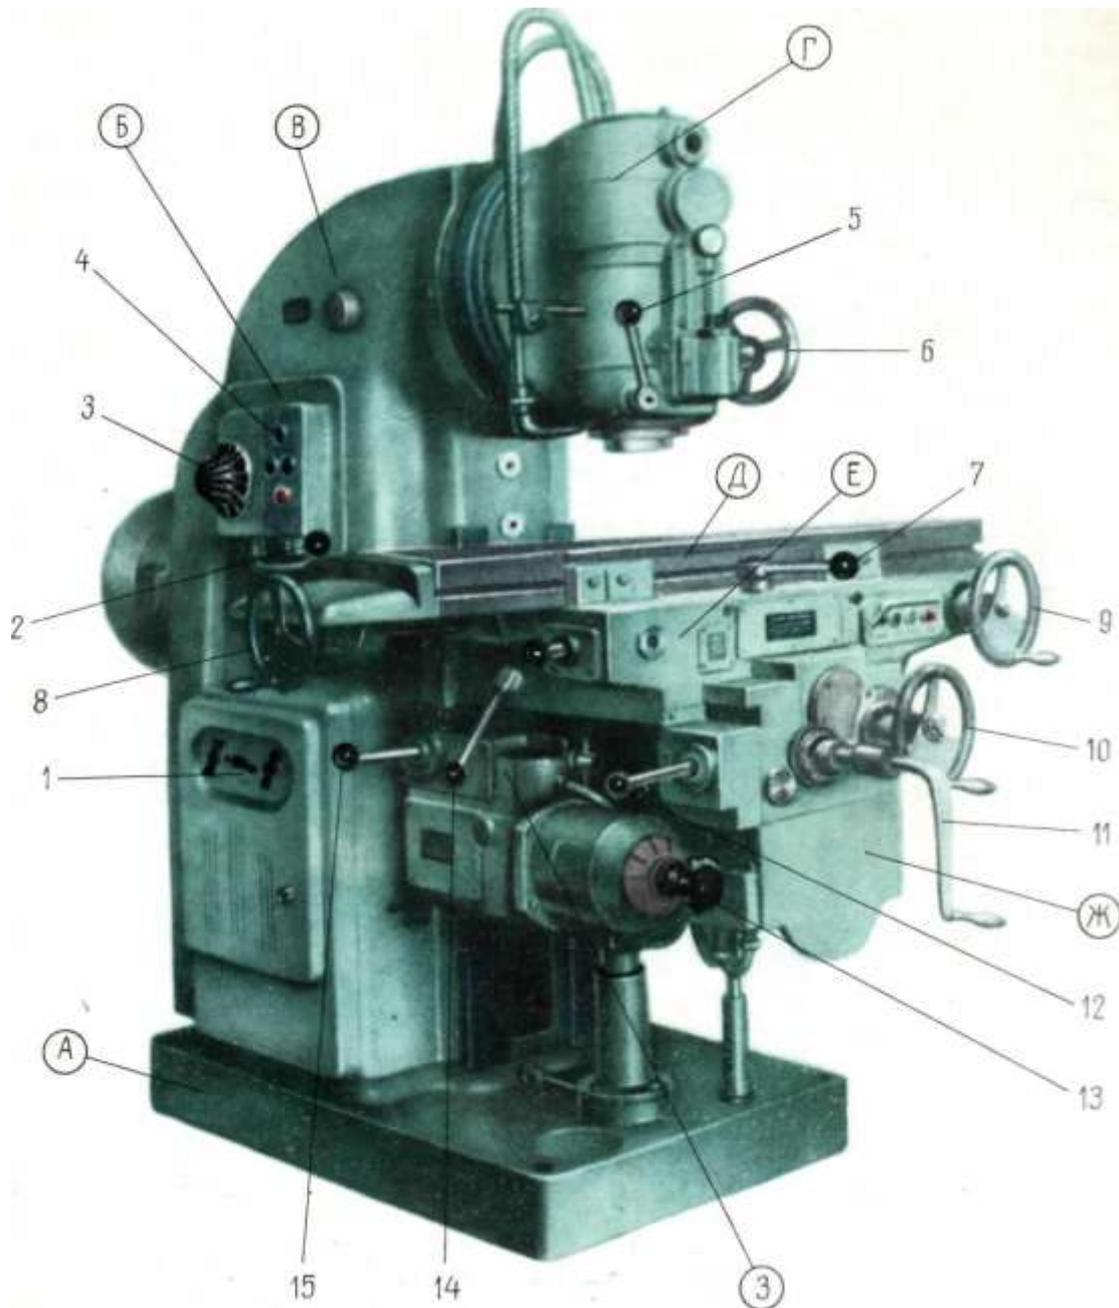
Общий вид вертикально-фрезерного станка модели 6Н12ПБ
